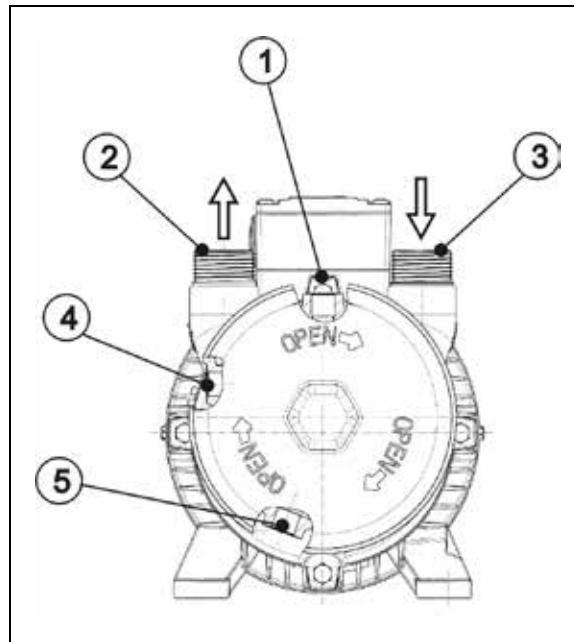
Rohr- / Schlauchanschlüsse der Vaku- umpumpe / des Kompressors
